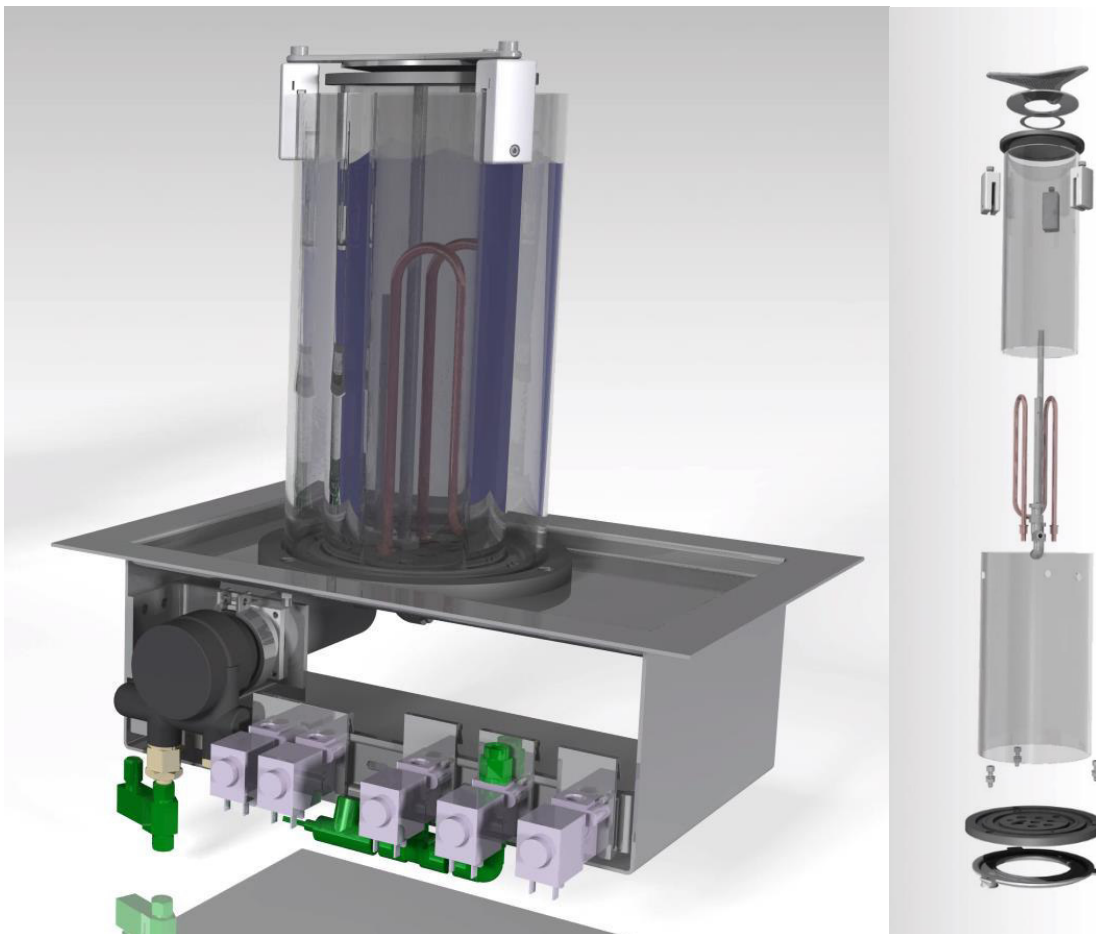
Borosilikatglasboiler mit Bodenblech und Verspannmechanismus (links) und Explosionszeichnung (rechts)
